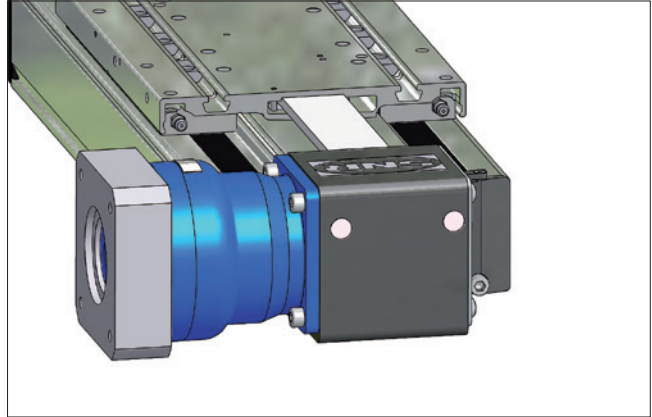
AXDL mit integriertem Planetengetriebe
